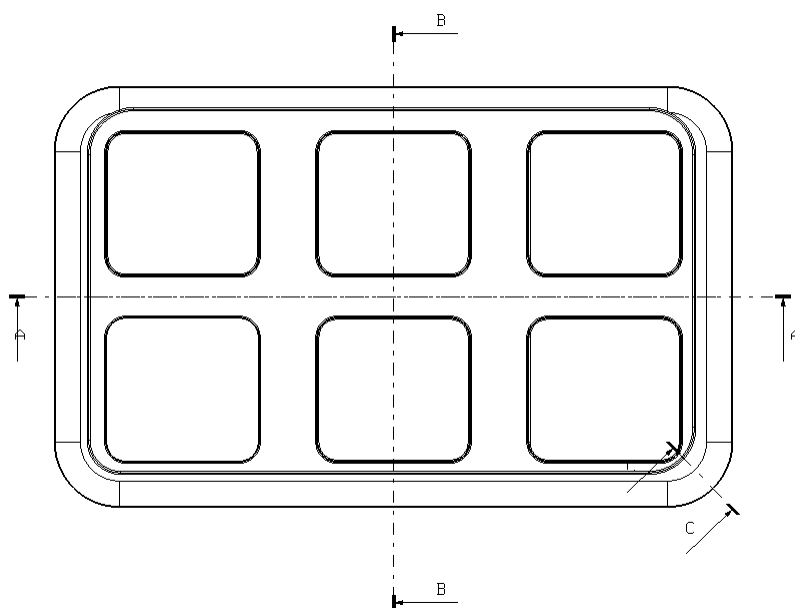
Розташування перерізів для вимірювання товщини стінки
